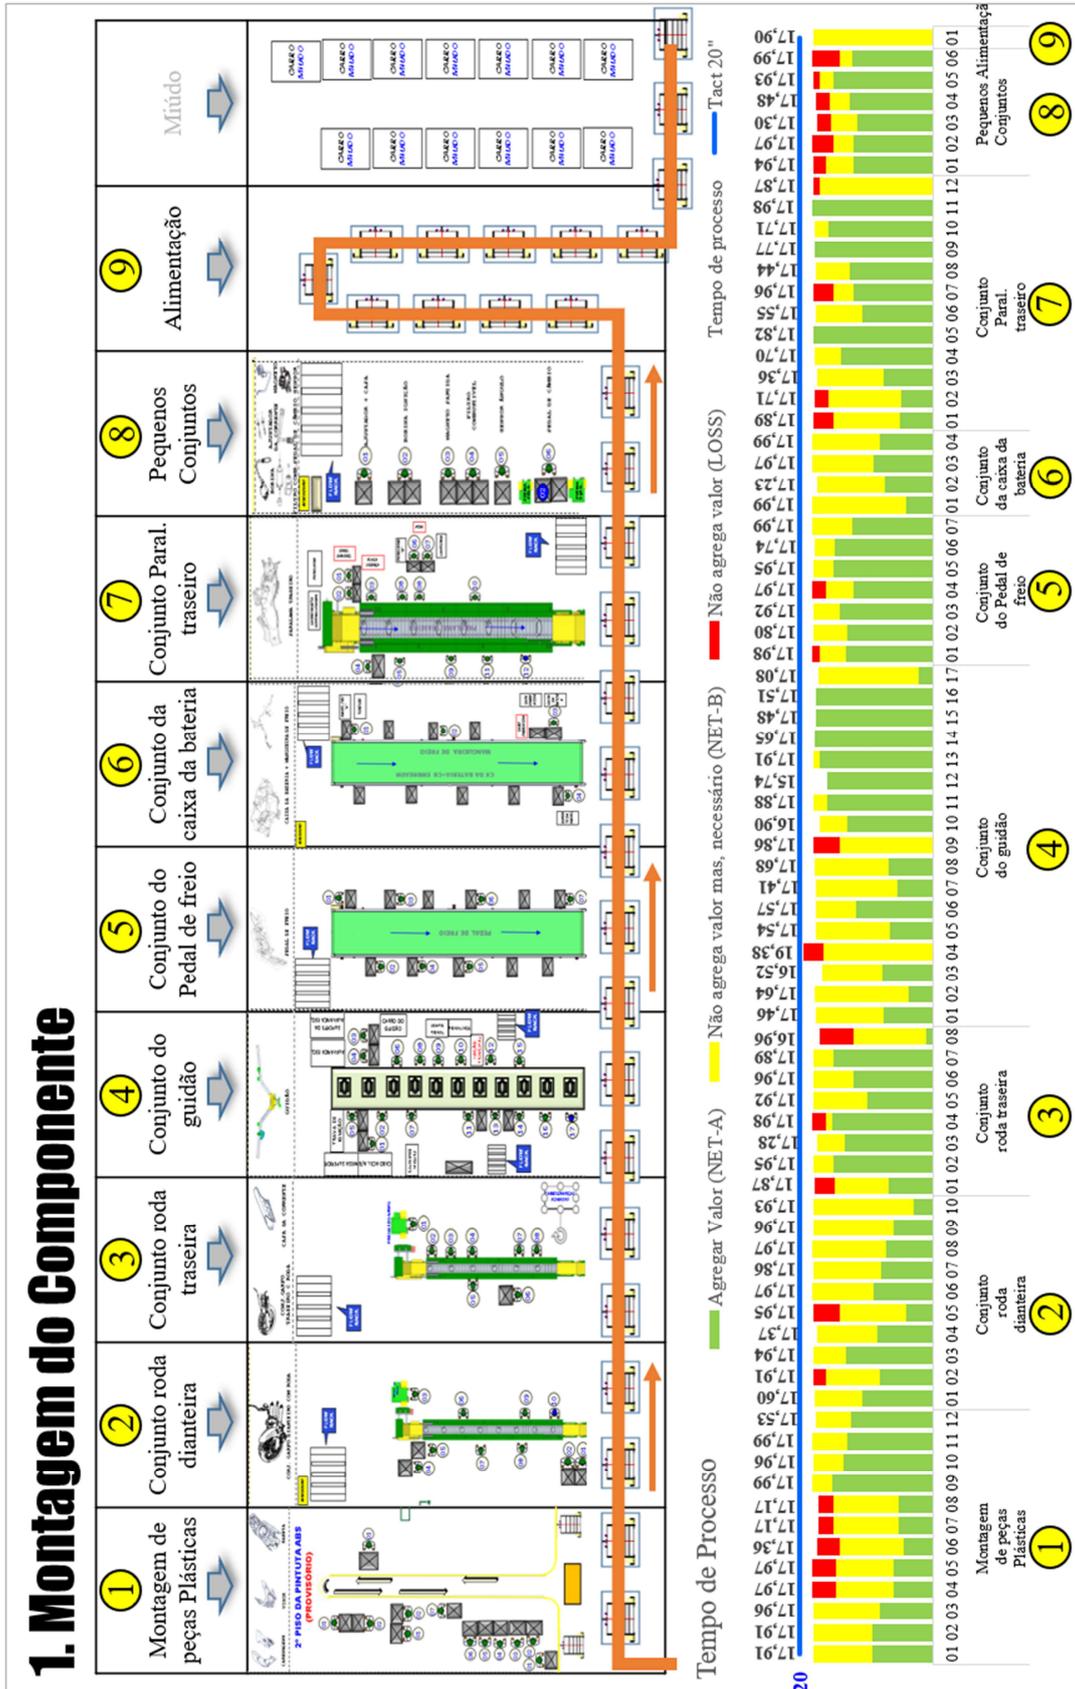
Layout da Cadeia da Montagem Final LM1J
